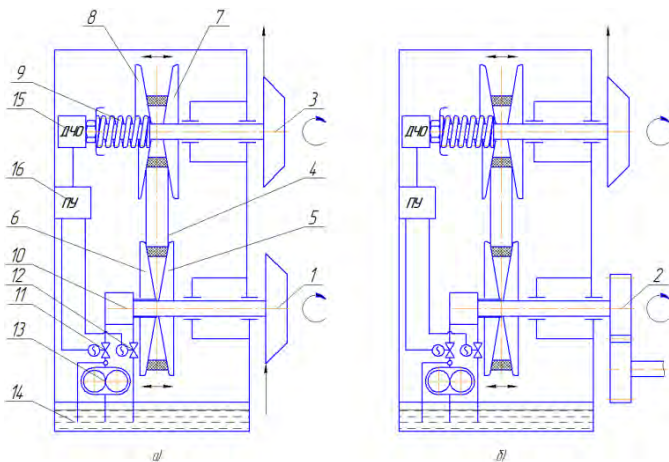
Турбокомпресор з газовою турбіною (а) та механічним приводом (б): 1 – газова турбіна; 2 – механічний привід; 3 – відцентровий компресор; 4 – ремінна передача; 5 – ведучий шків; 6, 8 – рухомий диск; 7 – ведений шків; 9 – пружина стискання; 10 – обертовий гідроциліндр; 11, 12 – електромагнітний клапан; 13 – масляний насос; 14 – масляна ванна; 15 – датчик частоти обертання; 16 – пульт управління
